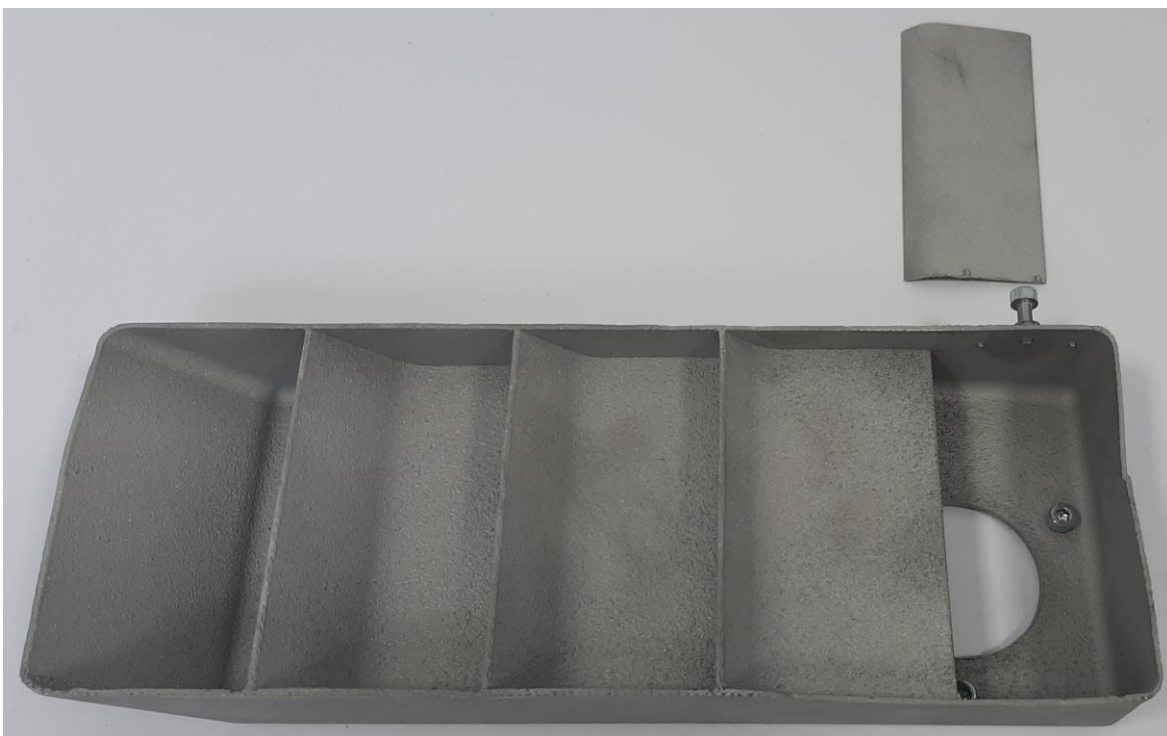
Detail spodného distribútoru prúdenia na stavebnej platforme.
